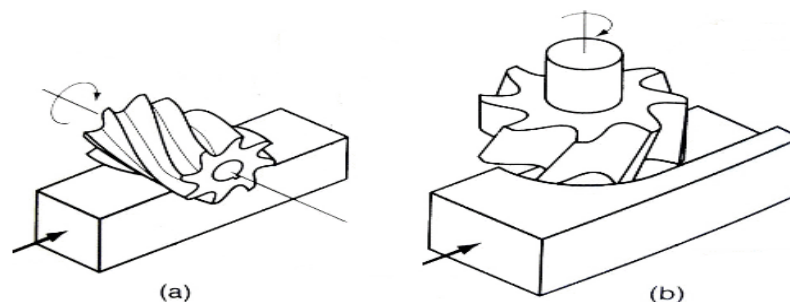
Fresagem cilíndrica (a) e fresagem de topo (b)
